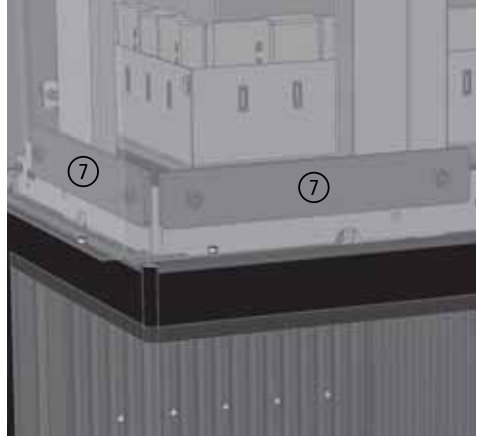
eingehängte Türgewichte bei KALA H ES
